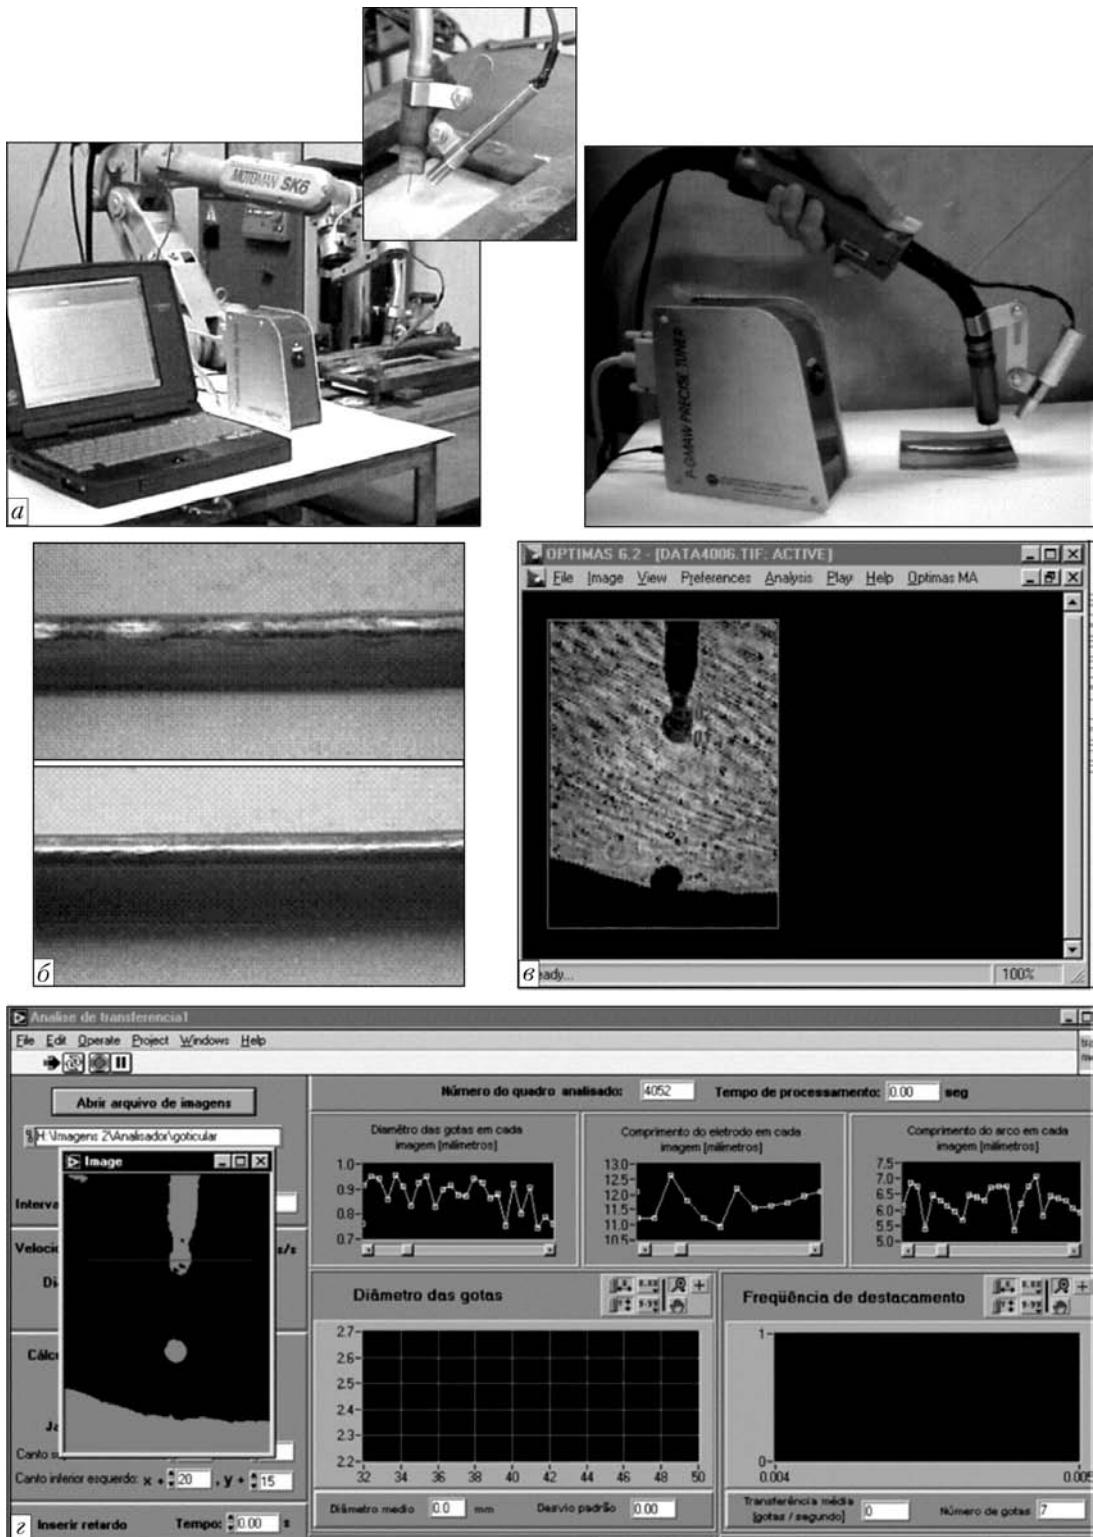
Система контроля (ручная сварка) и управления (автоматическая сварка) для обеспечения режима переноса электродного металла — одна капля за импульс при импульсно-дуговой сварке МИГ/МАГ, разработано для «White Martins» (а); б — вверху шов, выполненный плазменной сваркой с использованием в качестве плазмообразующего газа аргона (скорость сварки — 600 мм/мин), внизу аналогичный шов, выполненный на таком же токе сварки с использованием газа Stargold Flash, разработанного для «White Martins», который обеспечивает лучшее формирование и более высокие скорости сварки (2200 мм/мин); в — программа для определения текущего положения капель, измерения их скорости и ускорения; г — программа для измерения размеров капель, частоты их переноса, а также длины дуги
